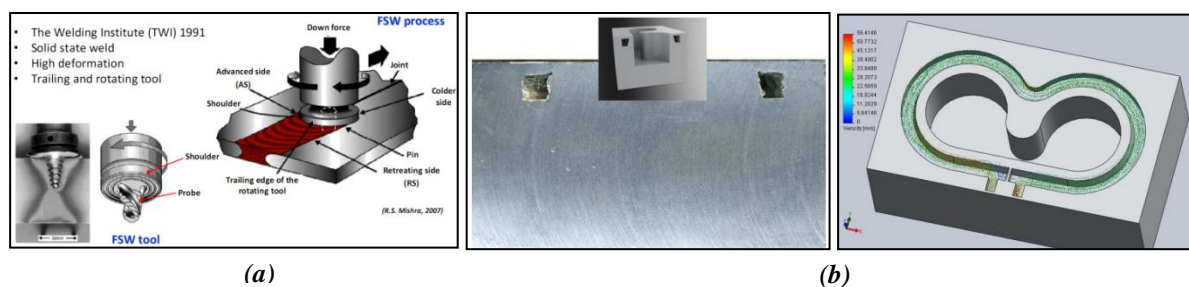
Princípio da soldagem Friction Stir Welding (a) e confecção de canais por Friction Stir Channelling (b) (QUINTINO, L.; VILAÇA P.; MIRANDA R, 2011)
